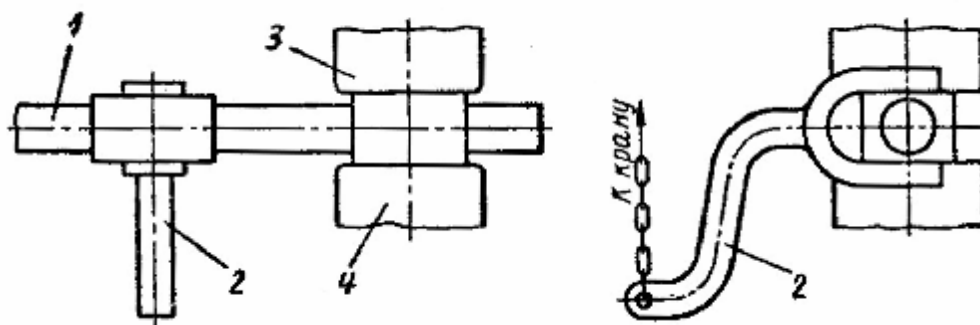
Схема скручивания: 1- груз (противовес), 2- изогнутая вилка, 3- верхний боек, 4- нижний боек
